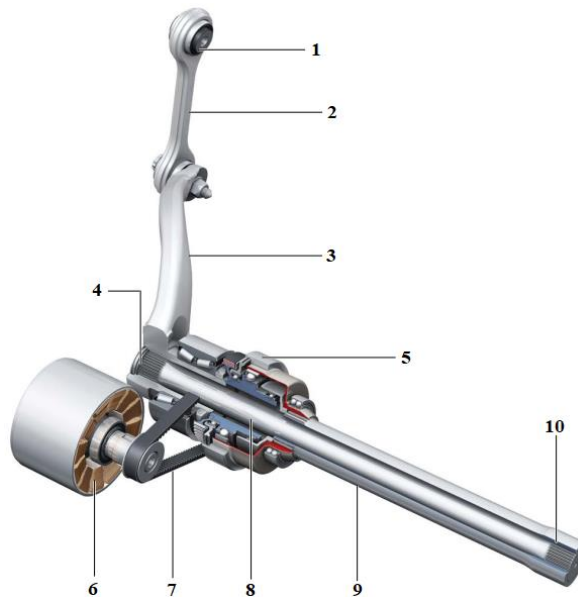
Конструкція електромеханічного стабілізатора крену: 1 - підшипник; 2 – верхня тяга; 3 – нижня тяга; 4 – торсіон; 5 – приводний механізм; 6 – електромотор; 7 – зубчастий ремінь; 8 – торсіонна штанга; 9 – торсіонна трубка; 10 – сполучна тяга.
